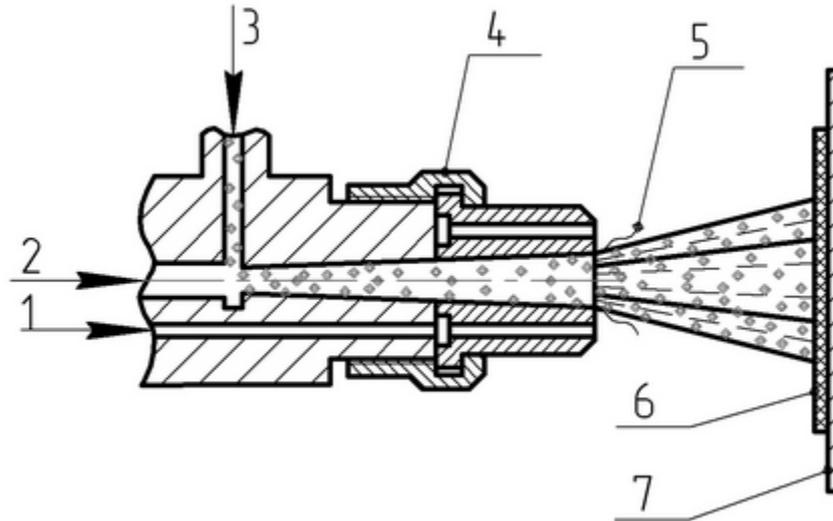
Схема газопламенного напыления: 1 – кислород и горючий газ; 2 – транспортирующий газ; 3 – напыляемый порошок; 4 – сопло; 5 – факел газового пламени; 6 – напыленное покрытие; 7 – напыляемая поверхность
